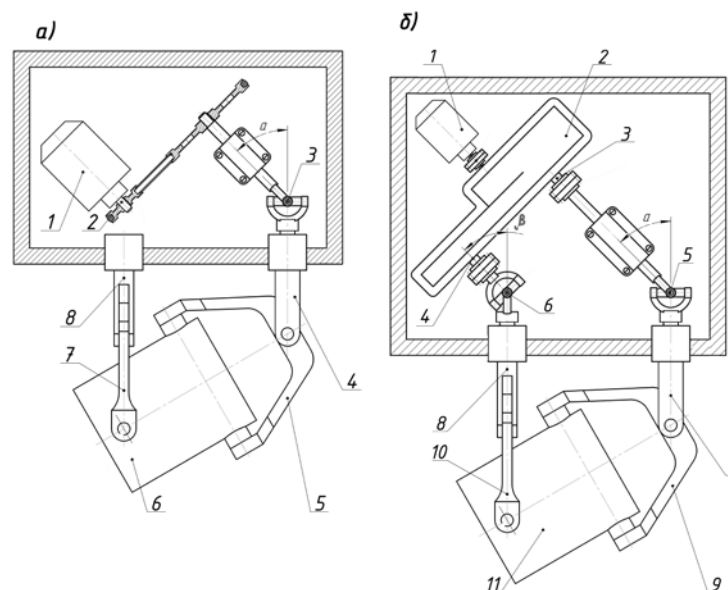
Машини зі складним рухом робочих ємкостей із застосуванням: а) приводу з шарніром Гука, б) з двома ведучими валами та двома шарнірами Гука
